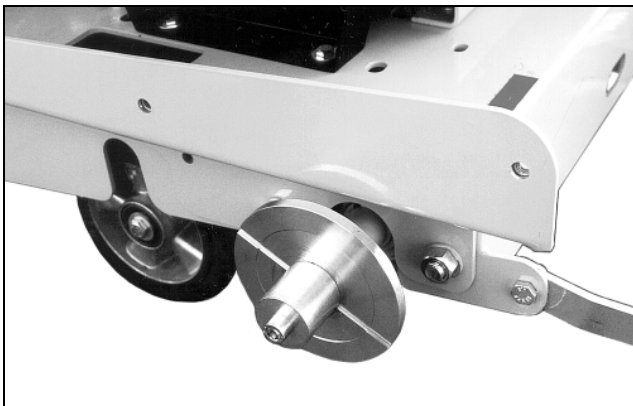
Вид фланца крепления режущего вала с противоположной стороны (фото без оснастки)
